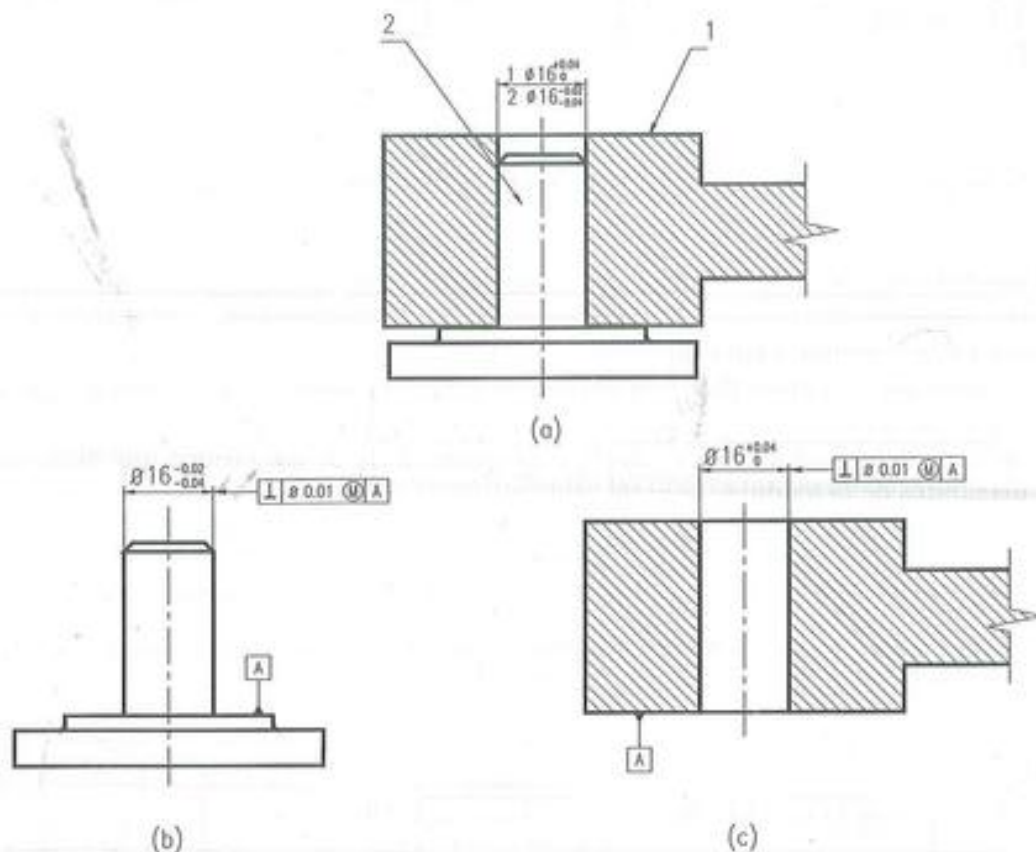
Combinación de ajustes y tolerancias geométricas de perpendicularidad.
